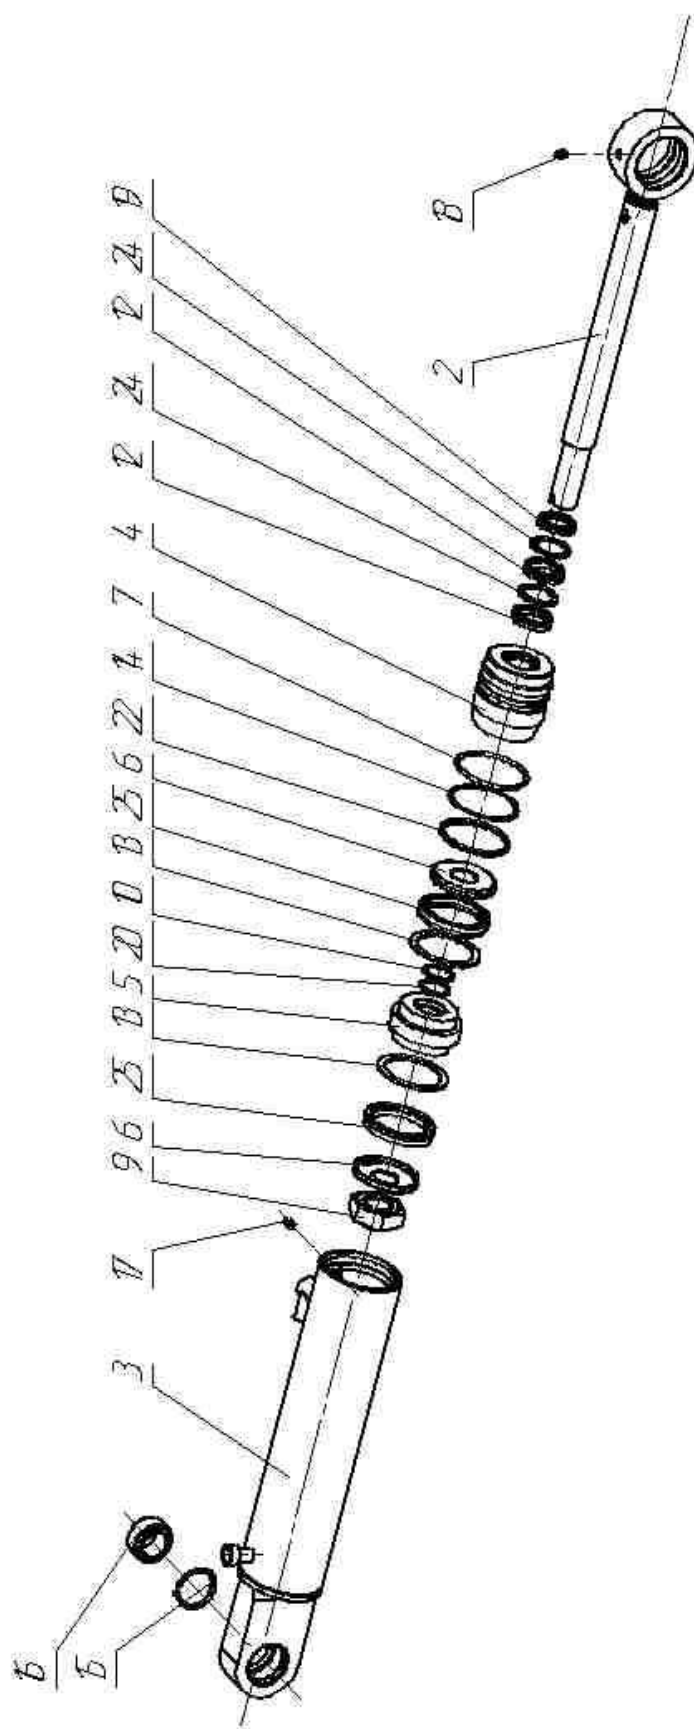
Гидроцилиндр поворота рабочего органа КРД-150311000
